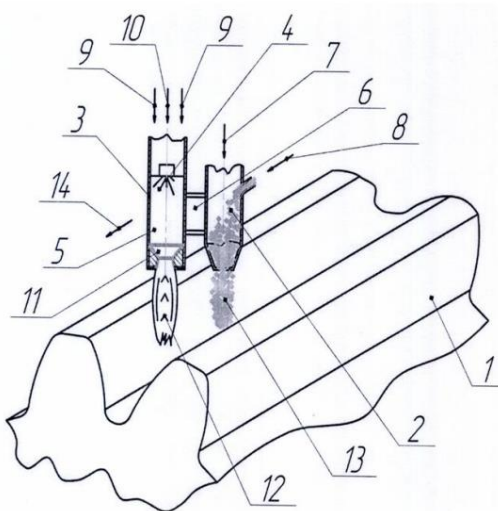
Устройство упрочнения зубчатых колес шаровых мельниц
